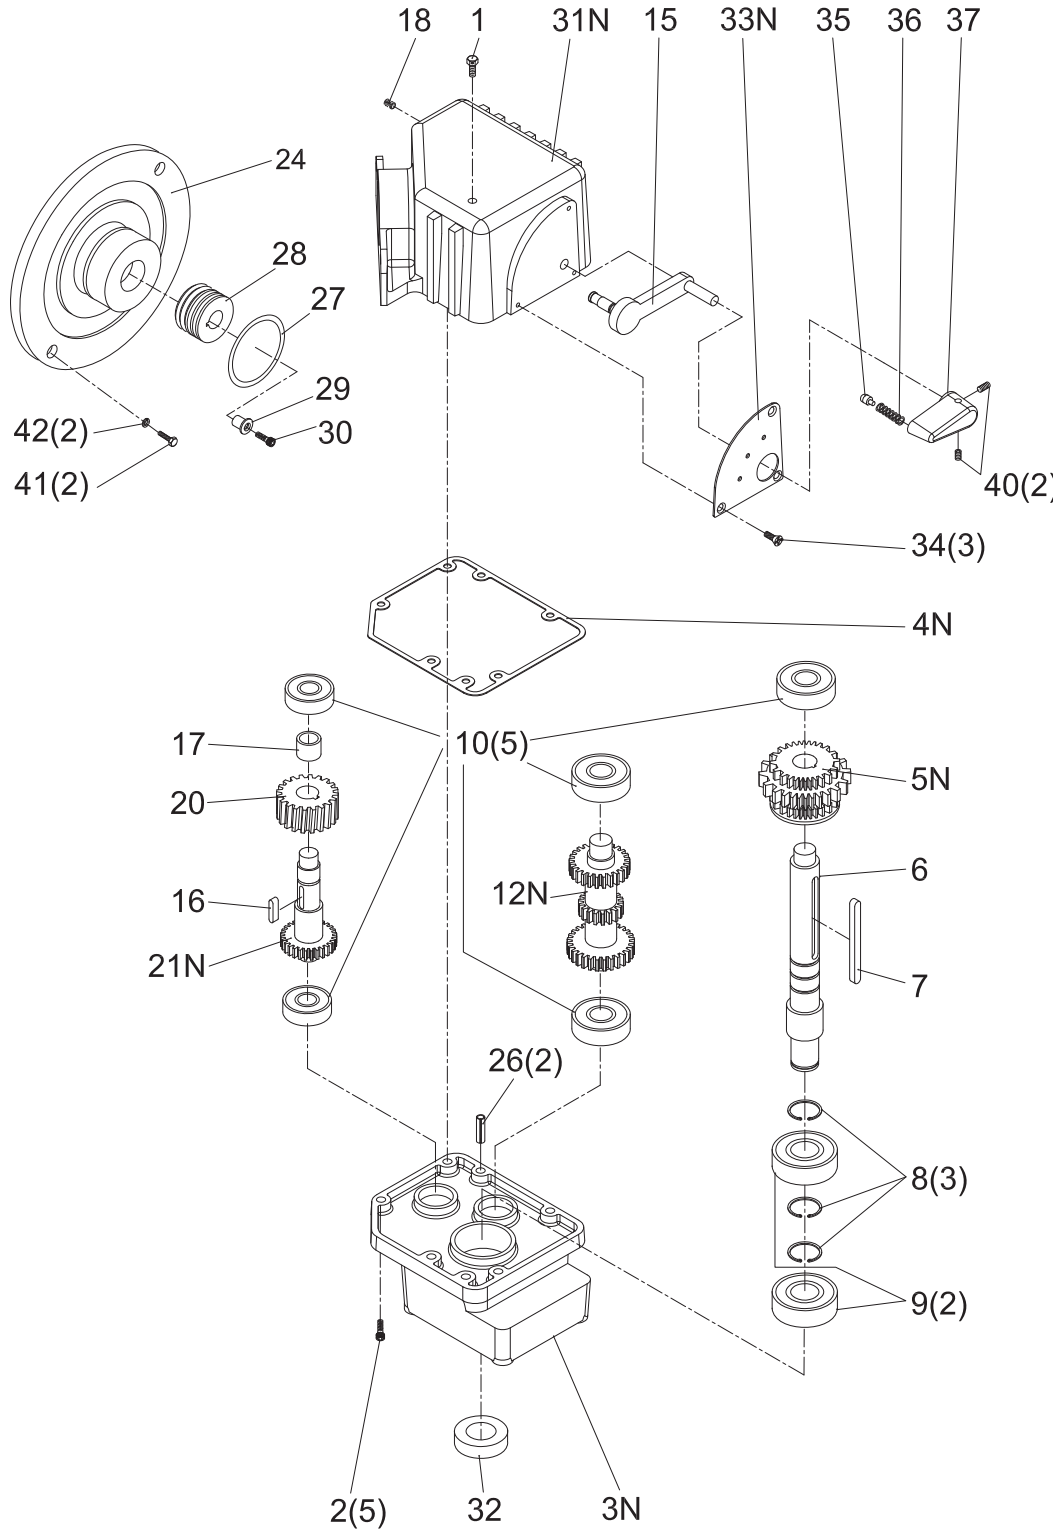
Explosionszeichnung Getriebe - Explosion drawing gear: 712 fifth generation
